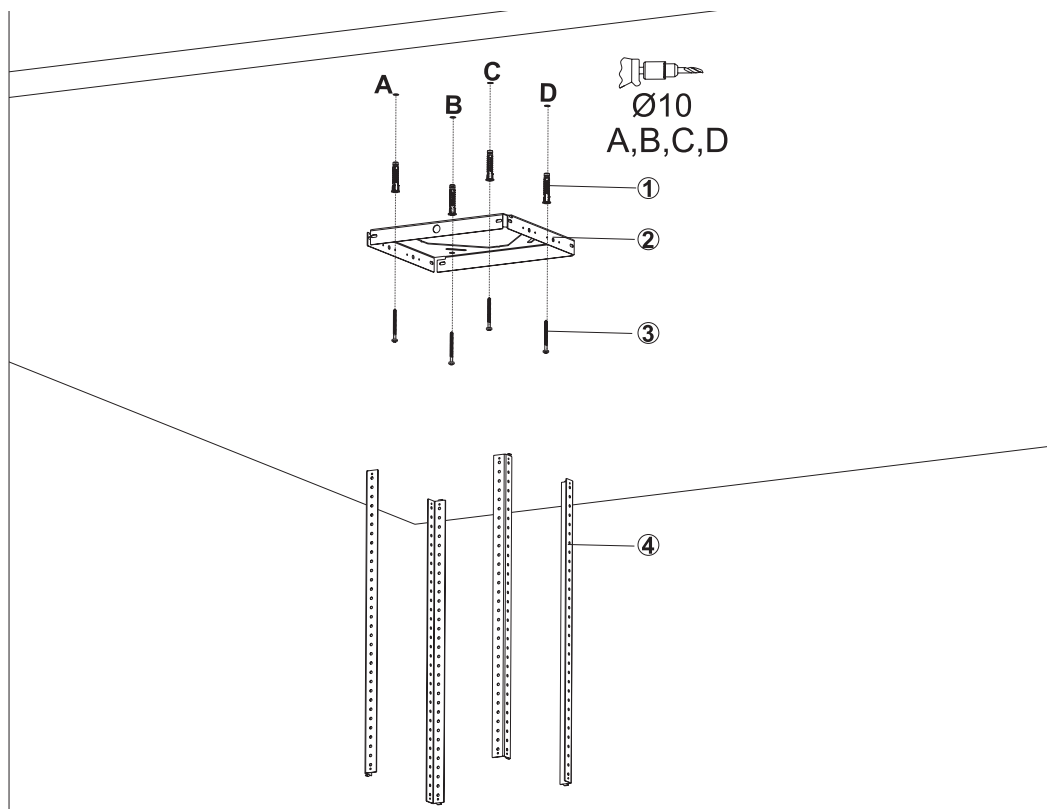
INSTALLAZIONE E COMPONENTI PARTE 1
